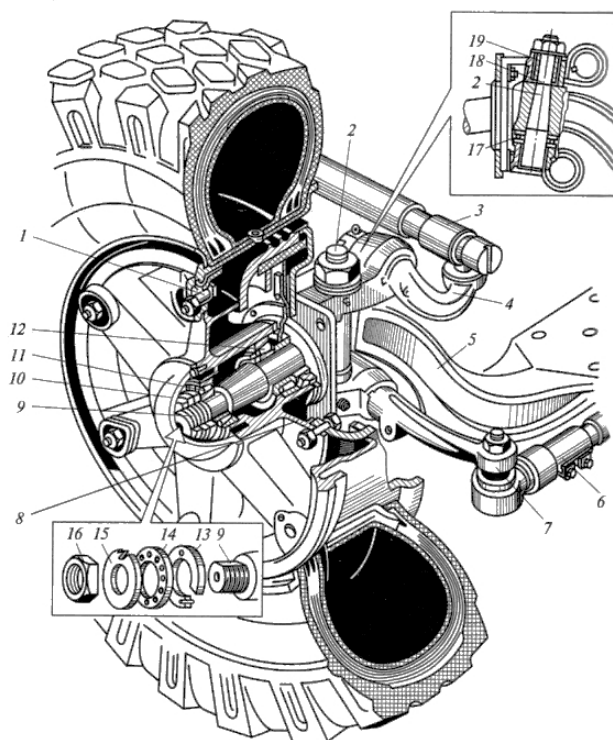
Передний управляемый мост автомобиля МАЗ: 1 — болт; 2 — шкворень; 3, 6 — рулевые тяги; 4, 7 — рычаги; 5 — балка; 8 — ступица; 9 — цапфа; 10 — колпак; 11, 12, 17 — подшипники; 13 — гайка; 14 — кольцо; 15 — шайба; 16 — контргайка; 18 — прокладка; 19 — втулка
